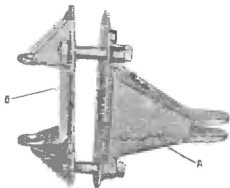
Нижний узел для подвешивания руля поворота, крепления качалок руля поворота и управления костью.
